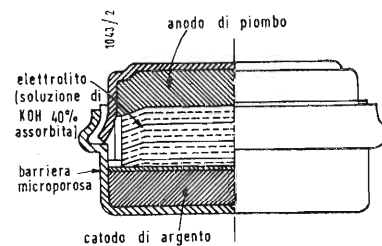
Sezione della pila ricaricabile Mallory XA-10B
